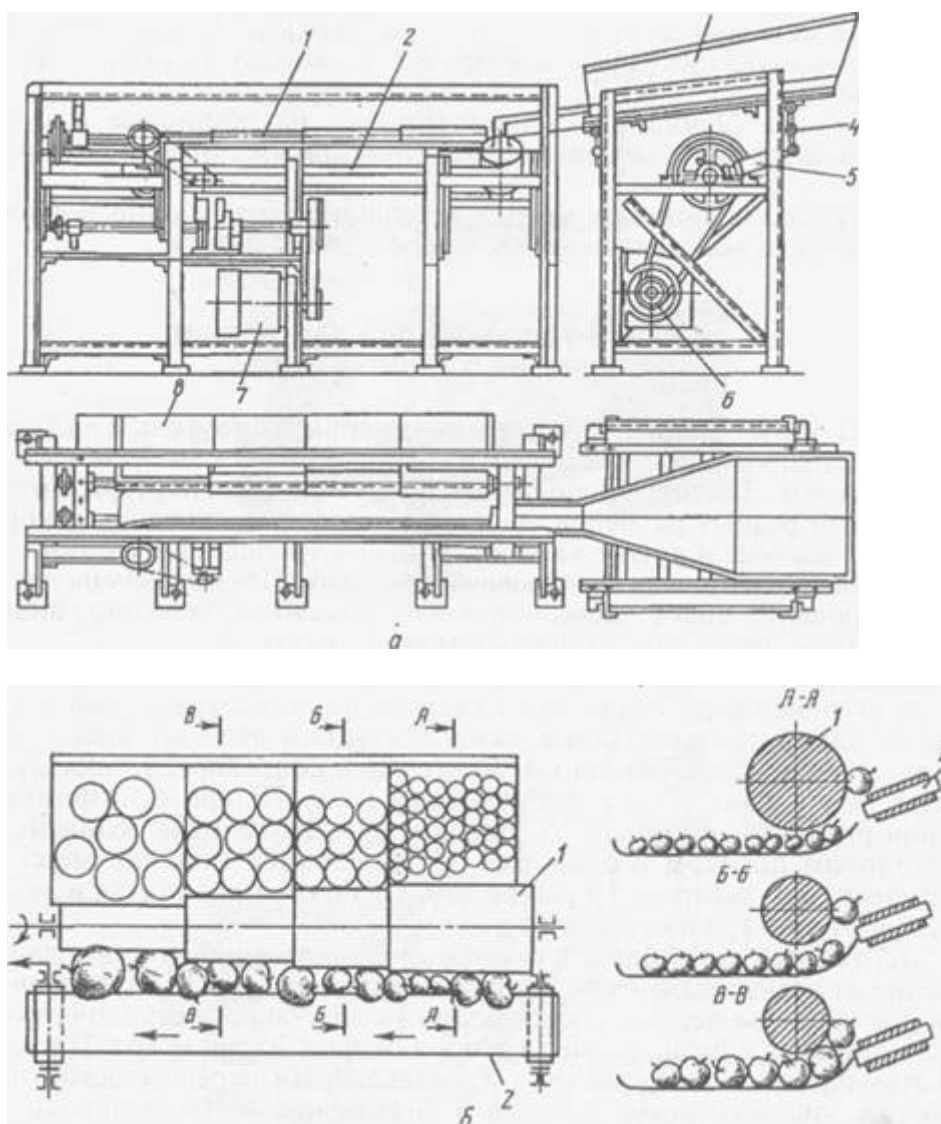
Валиколенточная калибровочная машина: а — конструкция;
